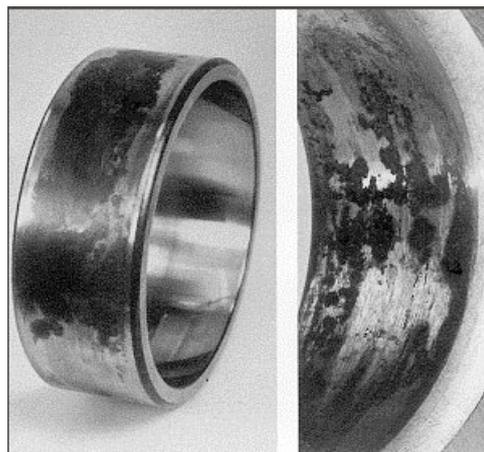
Разрушения от фреттинга на поверхности кольца подшипника
